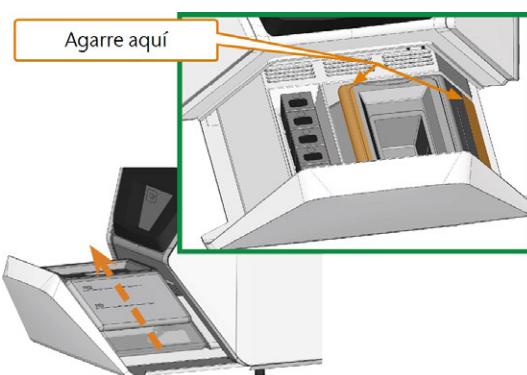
RETIRAR EL DEPÓSITO DE LÍQUIDO REFRIGERANTE DEL CAJÓN COMBINADO
